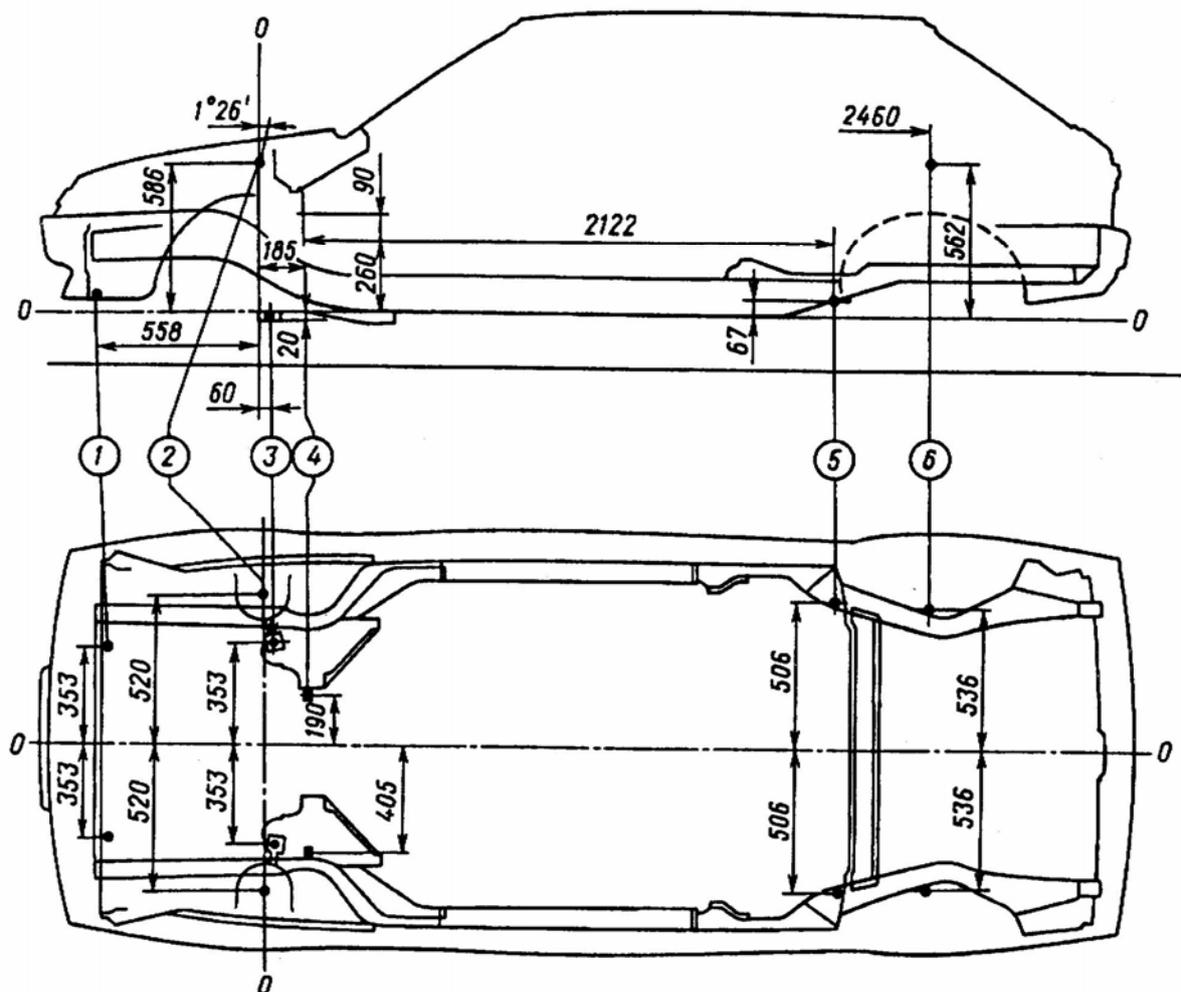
Основные размеры для проверки контрольных точек основания кузова автомобиля ВАЗ-2108: 1 – пересечение оси переднего болта крепления растяжки передней подвески с поверхностью панели рамки радиатора; 2 – центр верхнего шарнира стойки; 3 – центр шарнира рычага передней подвески; 4 – пересечение оси болтов крепления рулевого механизма с поверхностью заднего лонжерона; 5 – пересечение оси заднего болта крепления рычага задней подвески с поверхностью заднего лонжерона; 6 – центр верхней опоры амортизаторов задней подвески
